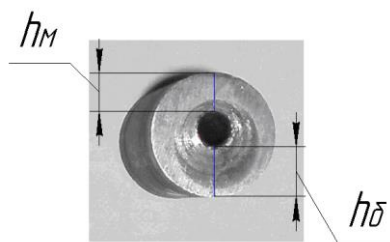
Разметка положений наибольшей и наименьшей толщины стенок на торце детали со стороны выхода инструмента
